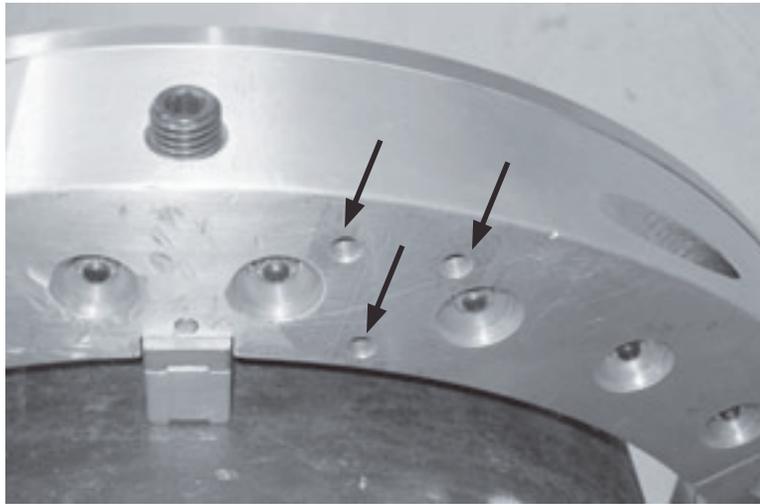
Das Foto zeigt die Komponenten des Werkzeugschlittens für unrunde Rohre.
